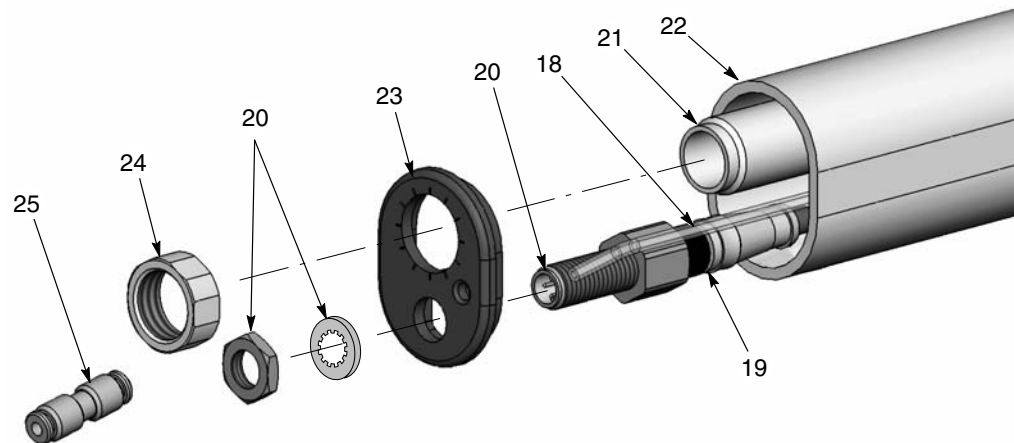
Desmontaje de la pistola de montaje en tubo 1 de 5
